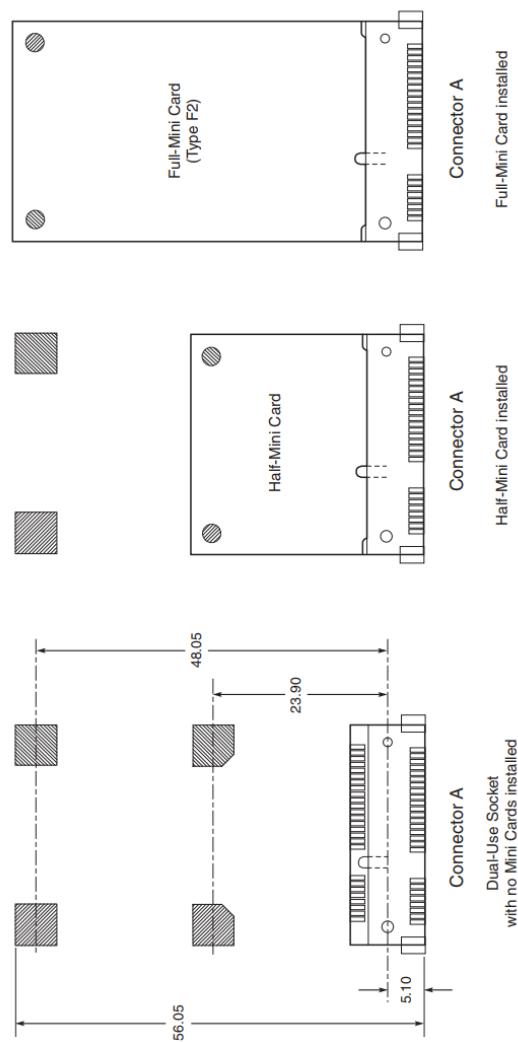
Emplacement générique pour carte PCI Express miniCard
